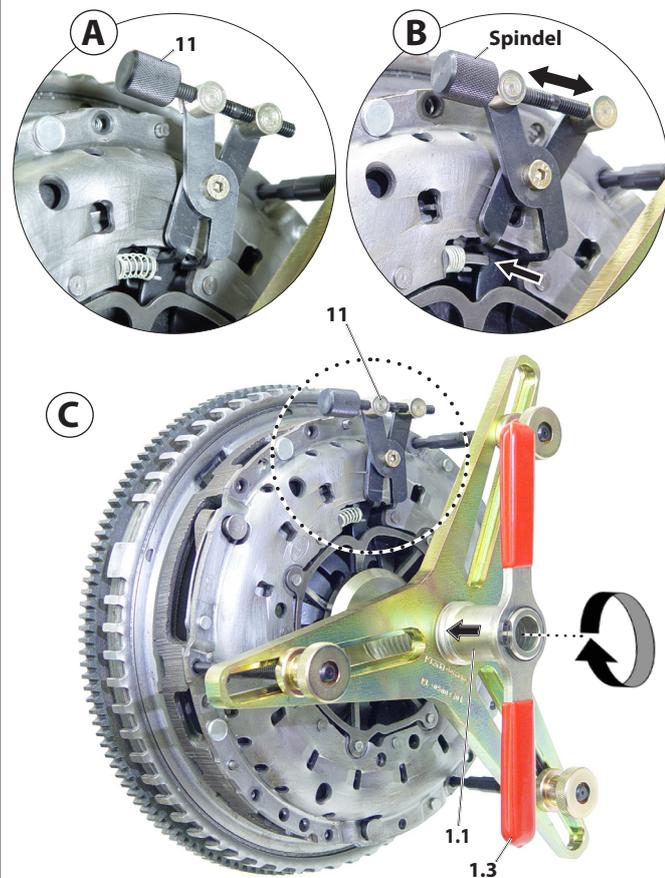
Alle Teile des SAC-Werkzeuges abbauen und entfernen.
